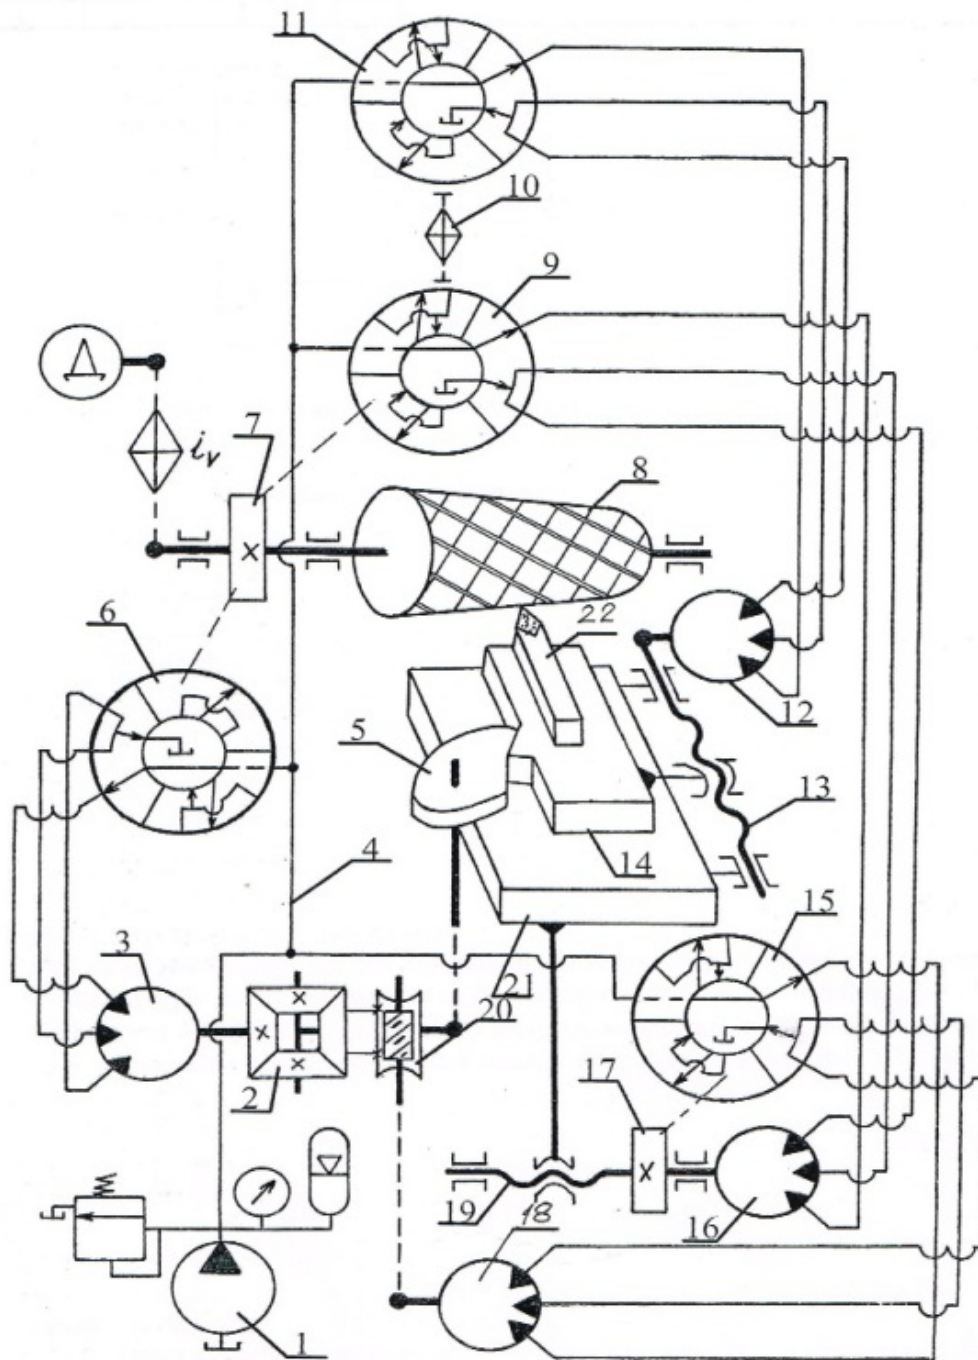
Структурная схема токарно-затыловочного станка для обработки конических резьбовых затылованных изделий с винтовыми стружечными канавками для обработки конических резьбовых затылованных изделий с винтовыми стружечными канавками
